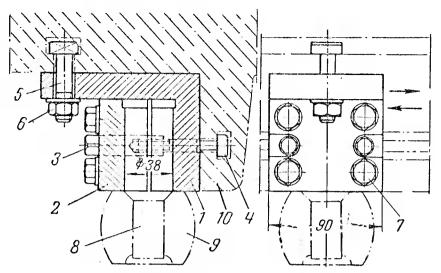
Пуансонодержатель одинарный передвижной. 1— корпус; 2— крышка; 3— гайка фасонная; 4, 5 и 7— болты; 6— гайка; 8— пуансон; 9— съемник резиновый; 10— плата подвижного стола.
